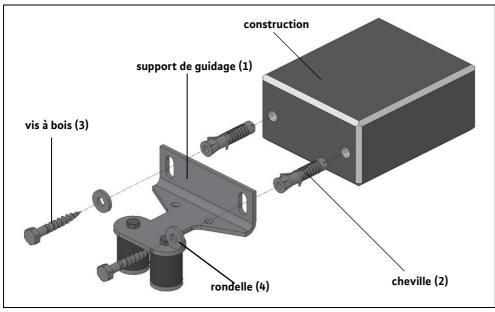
Montage du support de guidage pour fixation à la fosse
